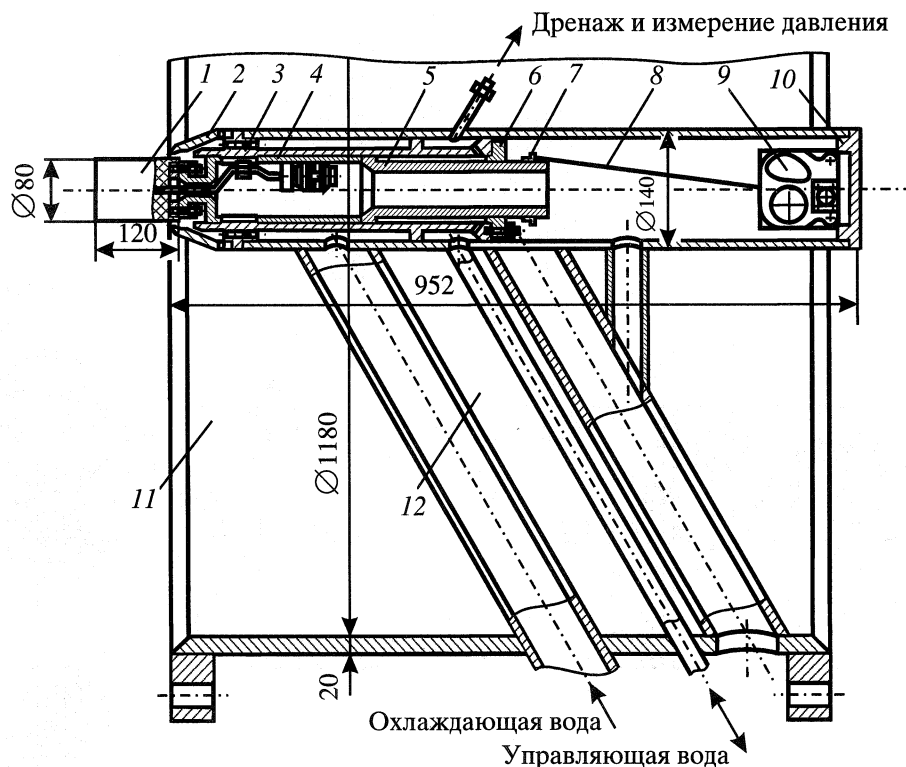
Конструкция державки: 1, 2 – стенки корпуса; 3 – пилон; 4 – поршень опорный; 5 – поршень управляющий; 6 – модель; 7 – крышка; 8 – гайка; 9 – датчик осевых перемещений; 10 – ежкторная труба; 11 – задняя крышка; 12 – тросик.
